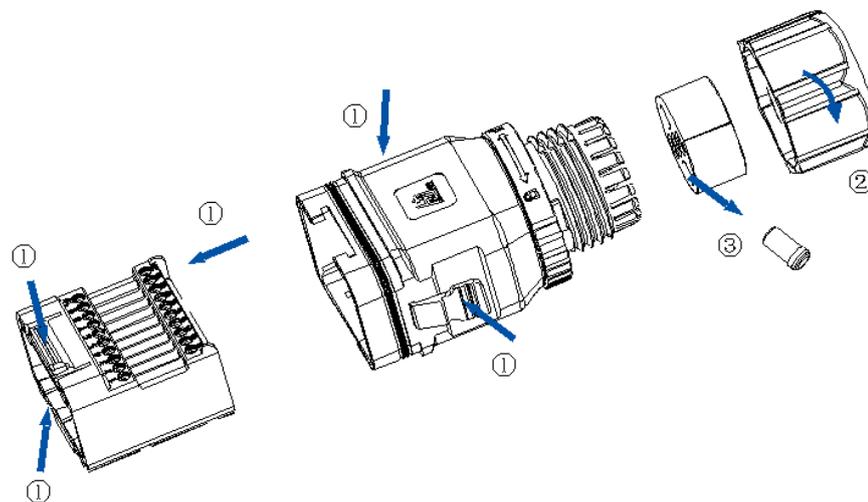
Desmontagem do conector do cabo de comunicação de 24 pinos
